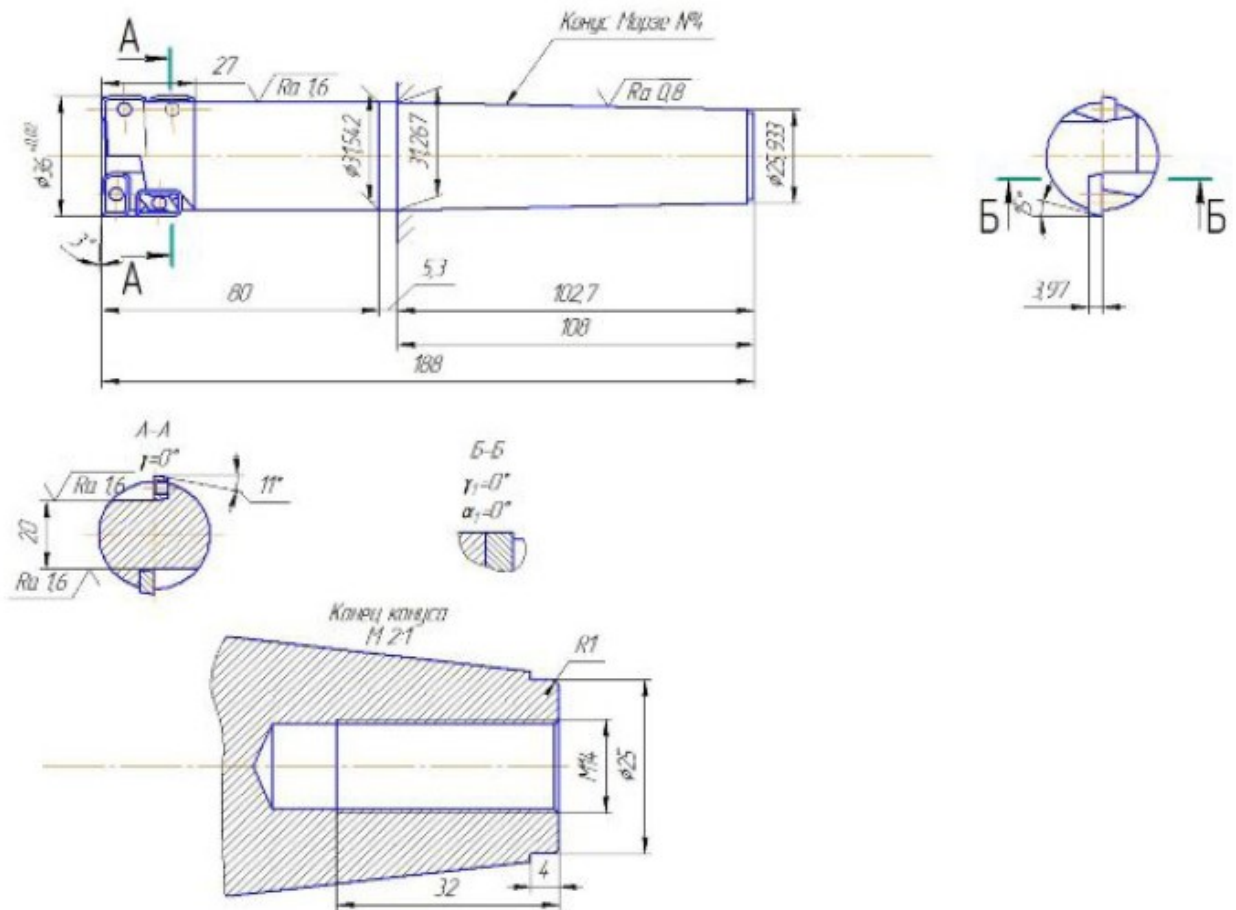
Фреза кінцева $\varnothing 36$ мм з механічним кріпленням пластин Т5К10
